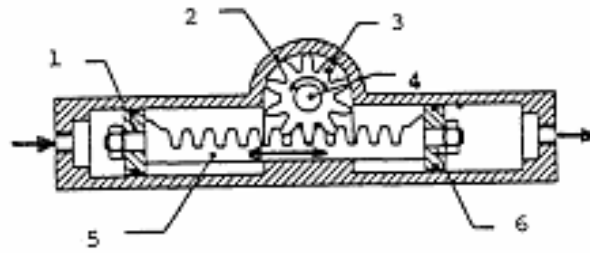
Motor Hidraulik Jenis Motor Roda Gigi
